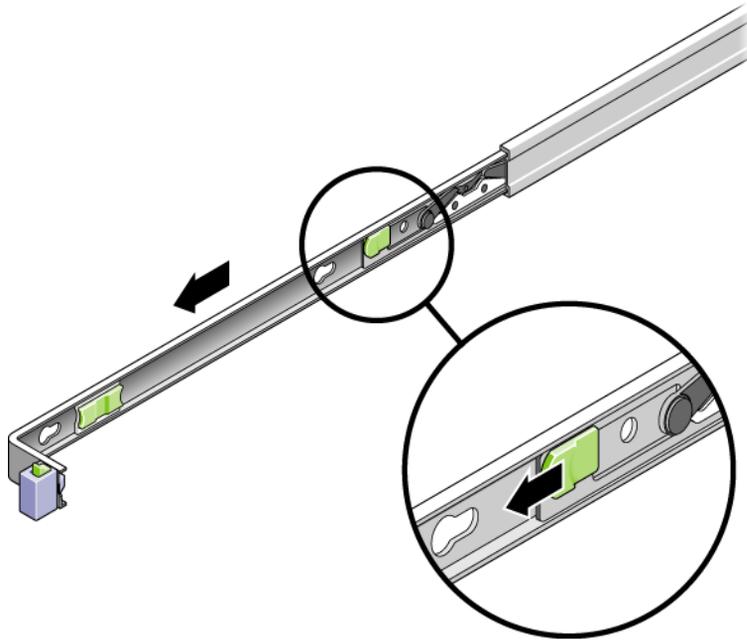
Emplacement du bouton de dégagement du support de montage
